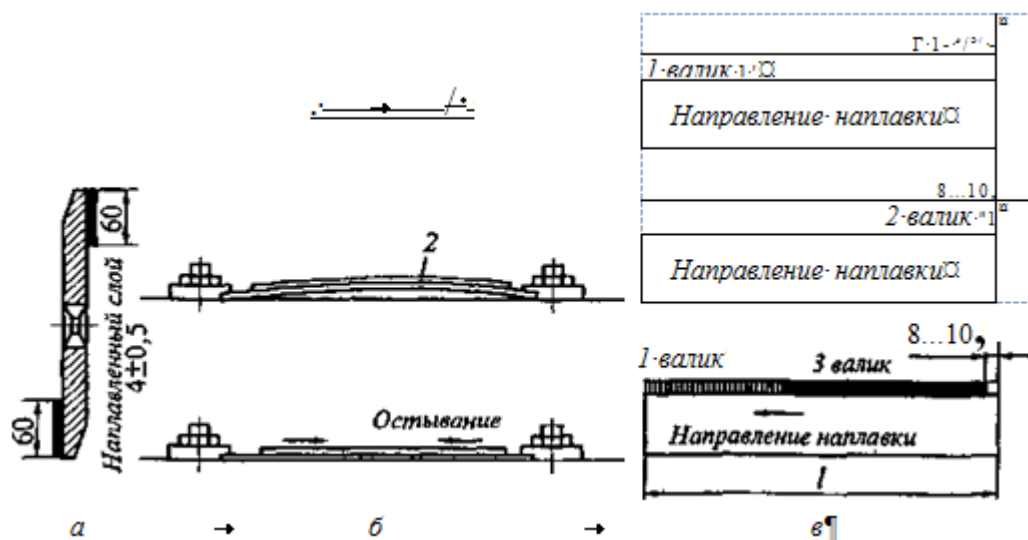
Схемы наплавки ножей бульдозеров и автогрейдеров:
